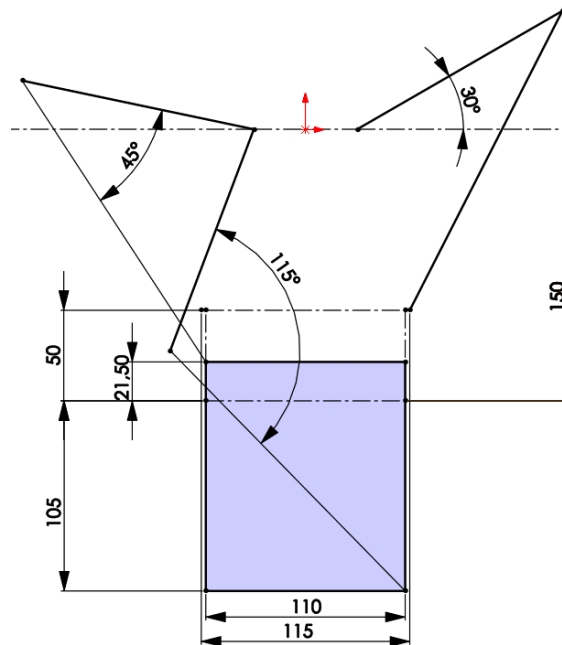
Condicions inicials del dimensionament (Font pròpia)
